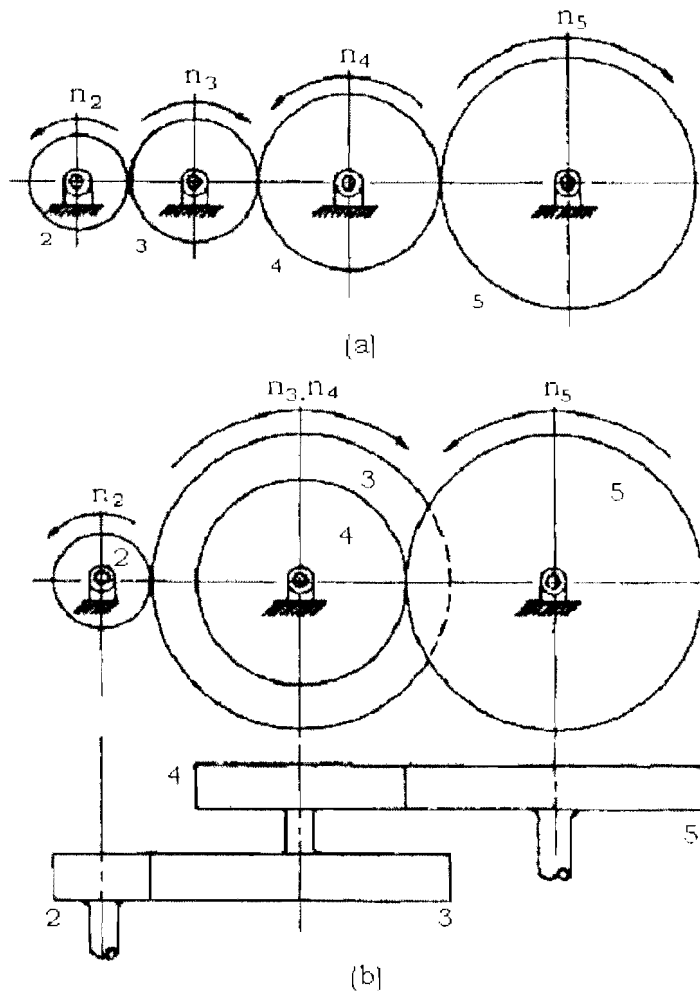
a) Tren de engranaje simple. b) tren de engranaje compuesto
